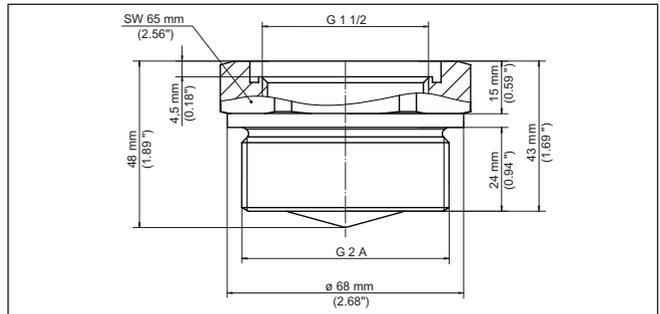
Dimensiones adaptador de rosca G1½ (DIN 3852-X) a rosca G2 (DIN 3852-X)
